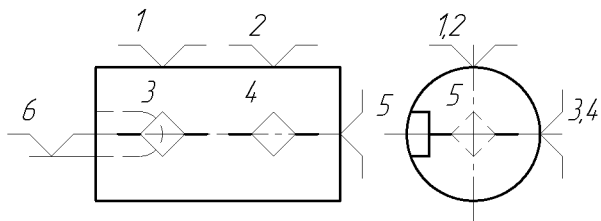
Теоретична схема базування довгих циліндричних деталей ($l > d$): 1,2,3,4 – подвійна напрямна база; 5 – опорна база; 6 – опорна база
